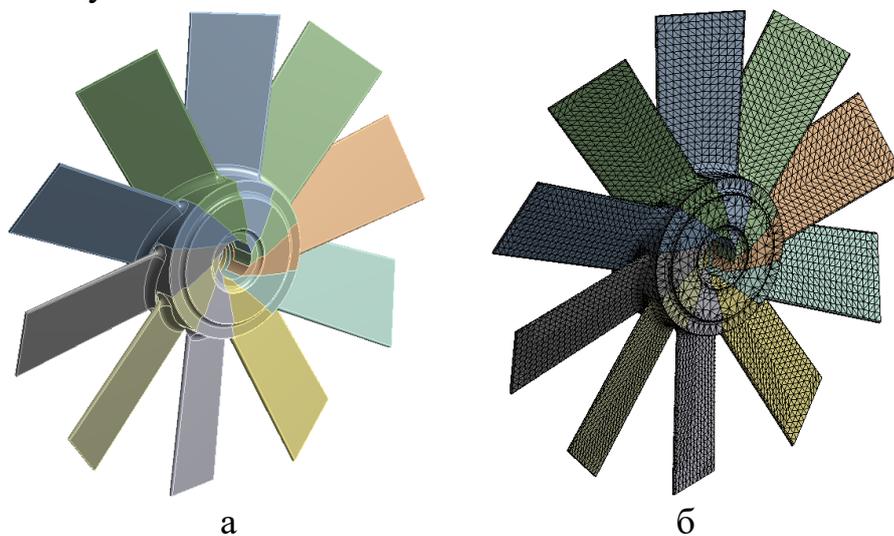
Академическое рабочее колесо с 10-ю лопатками
